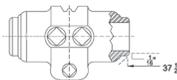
CC= Ambos extremos tipo Cuello Soldable (ANSI B16.5)
